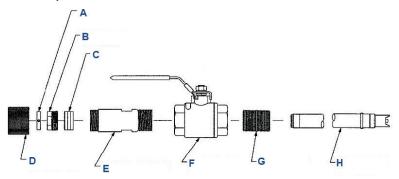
Kit gruppo valvola a sfera (n. pezzo 23765-00) e sensore
